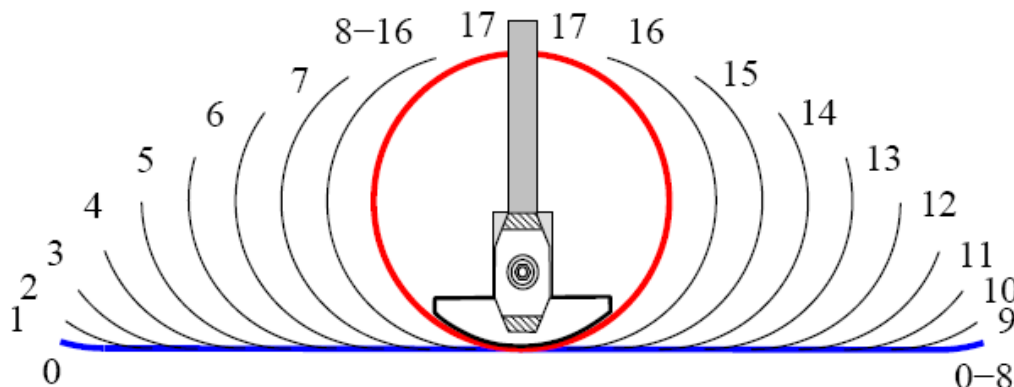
Последовательный вид заготовки при изгибе на прессе (17 ударов пуансона)
